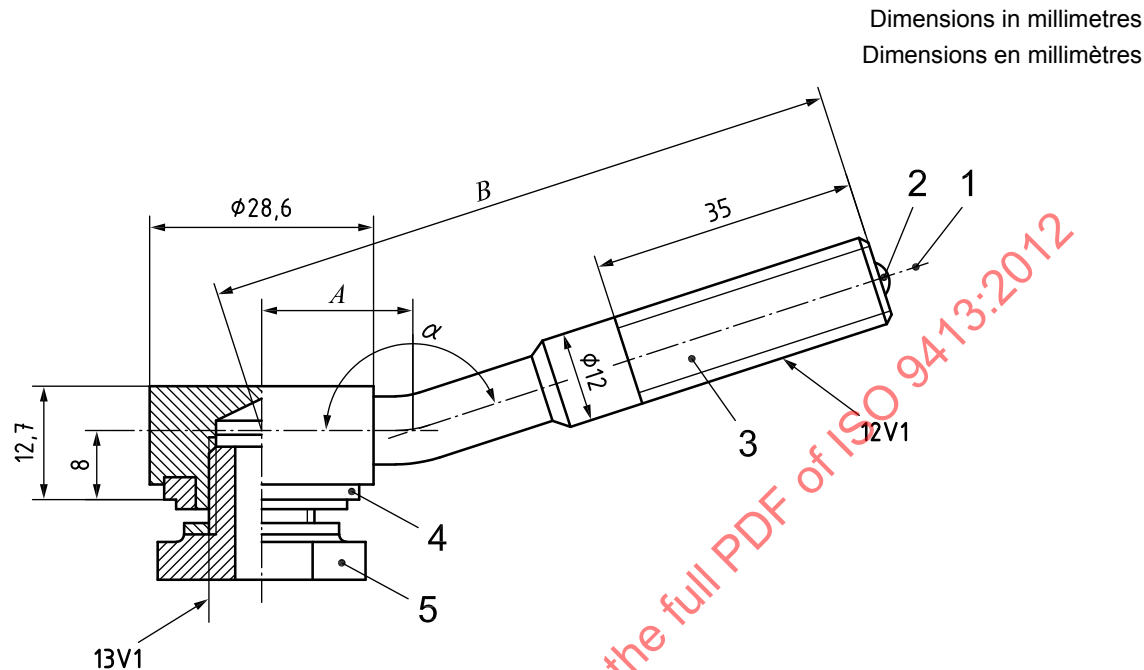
Montage de la valve tubeless air/liquide pour trou de valve pour la jante $15,7^{+0,4}_0$
